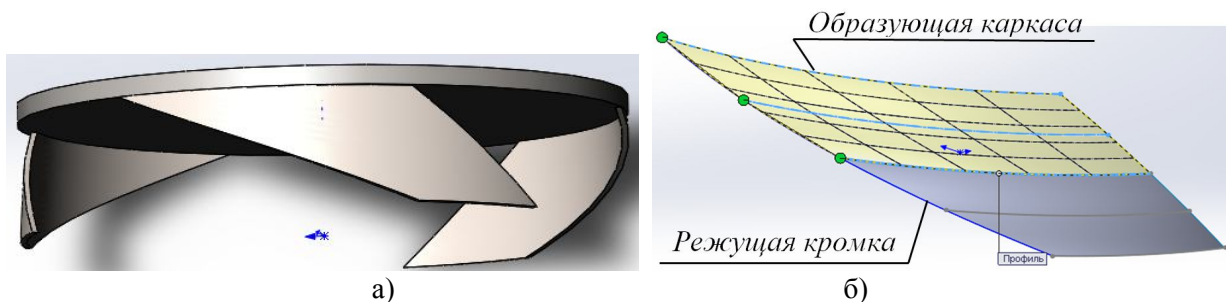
Формирование рабочей поверхности почвообрабатывающего элемента
